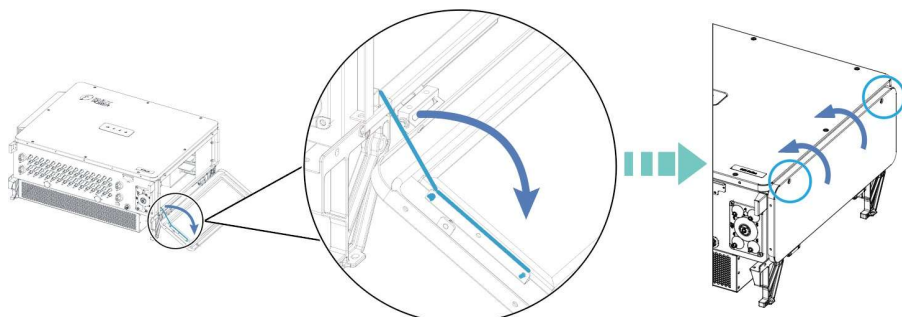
Recubrir la cubierta lateral de la caja de cables de CA
